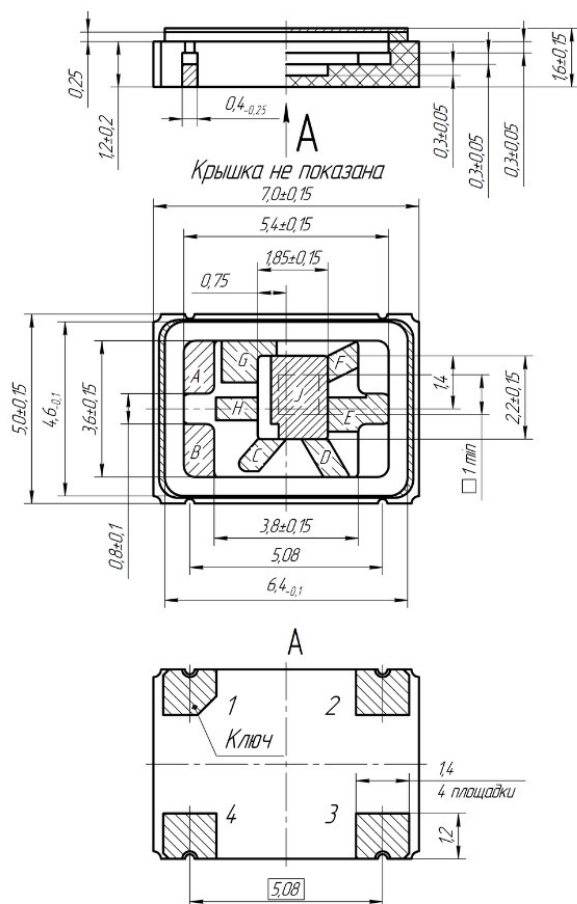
Внешний вид корпуса DLCC 8/4-3
